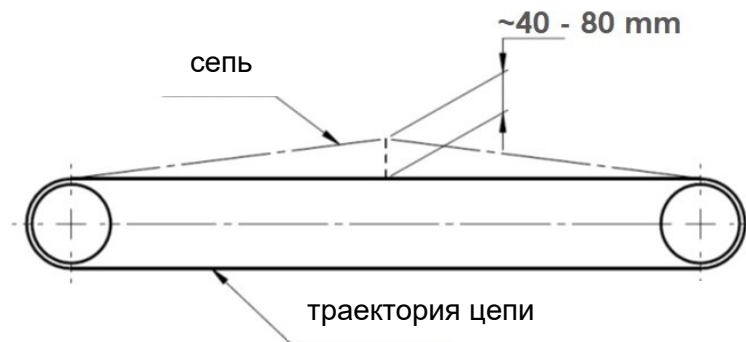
й Проверка натяжения цепи в разбрасывателе
